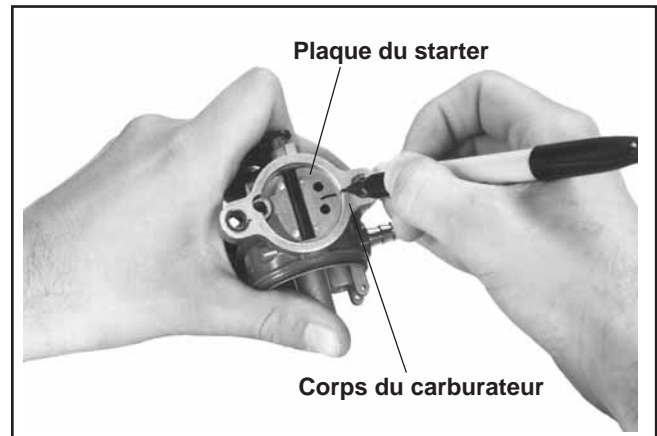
Marquage de la plaque du starter et du corps du carburateur.
